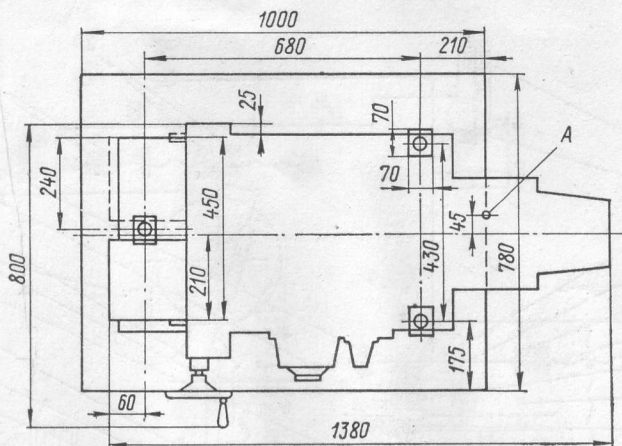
Габаритные размеры и план фундамента станка 7A311:
